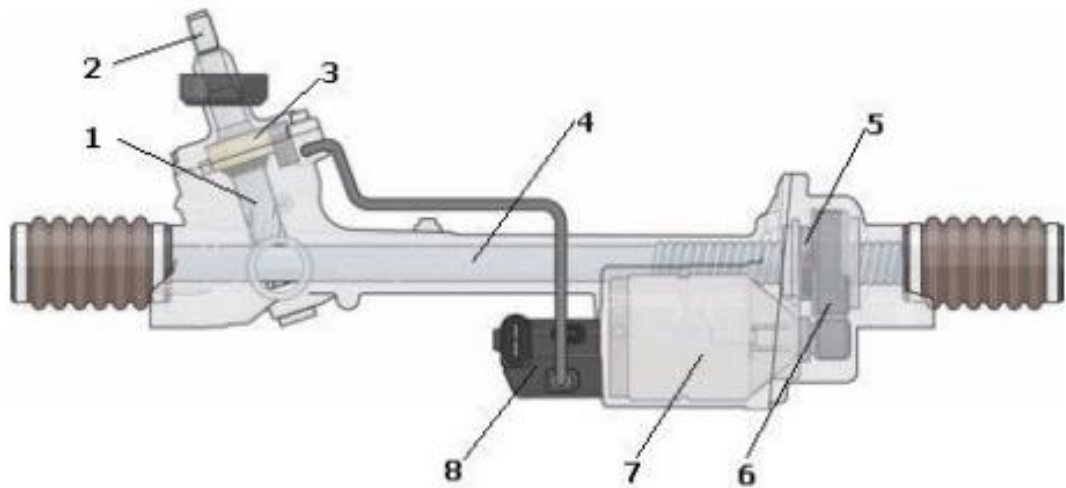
Схема ЕПК з паралельним приводом: 1 - вал із шестірнею РМ; 2 - вал керма; 3 - датчики моменту і кута повороту; 4 - рейка РМ; 5 - гайка на циркулюючих кульках; 6 - передача пасова; 7 - електричний двигун; 8 - електронний блок керування
